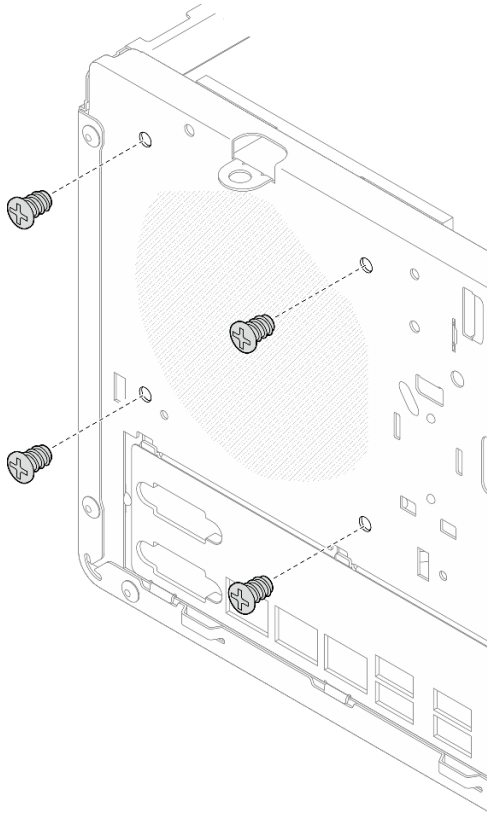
Installieren des Kühlkörper-Lüfters an der Gehäuserückseite
